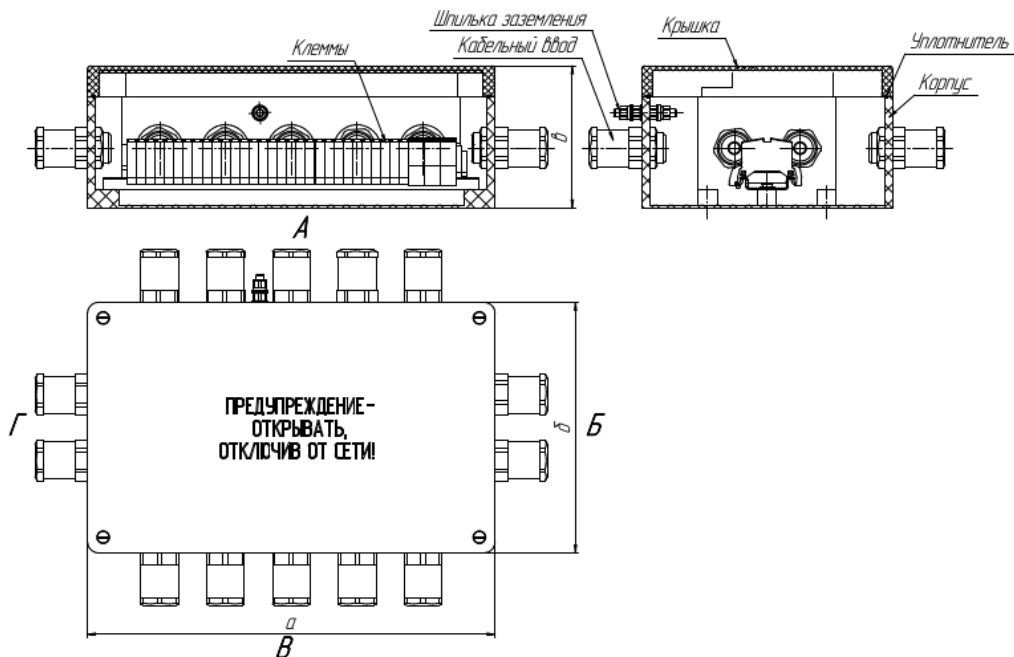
Общий вид , габаритные и присоединительные размеры клеммных коробок EhKK-II
